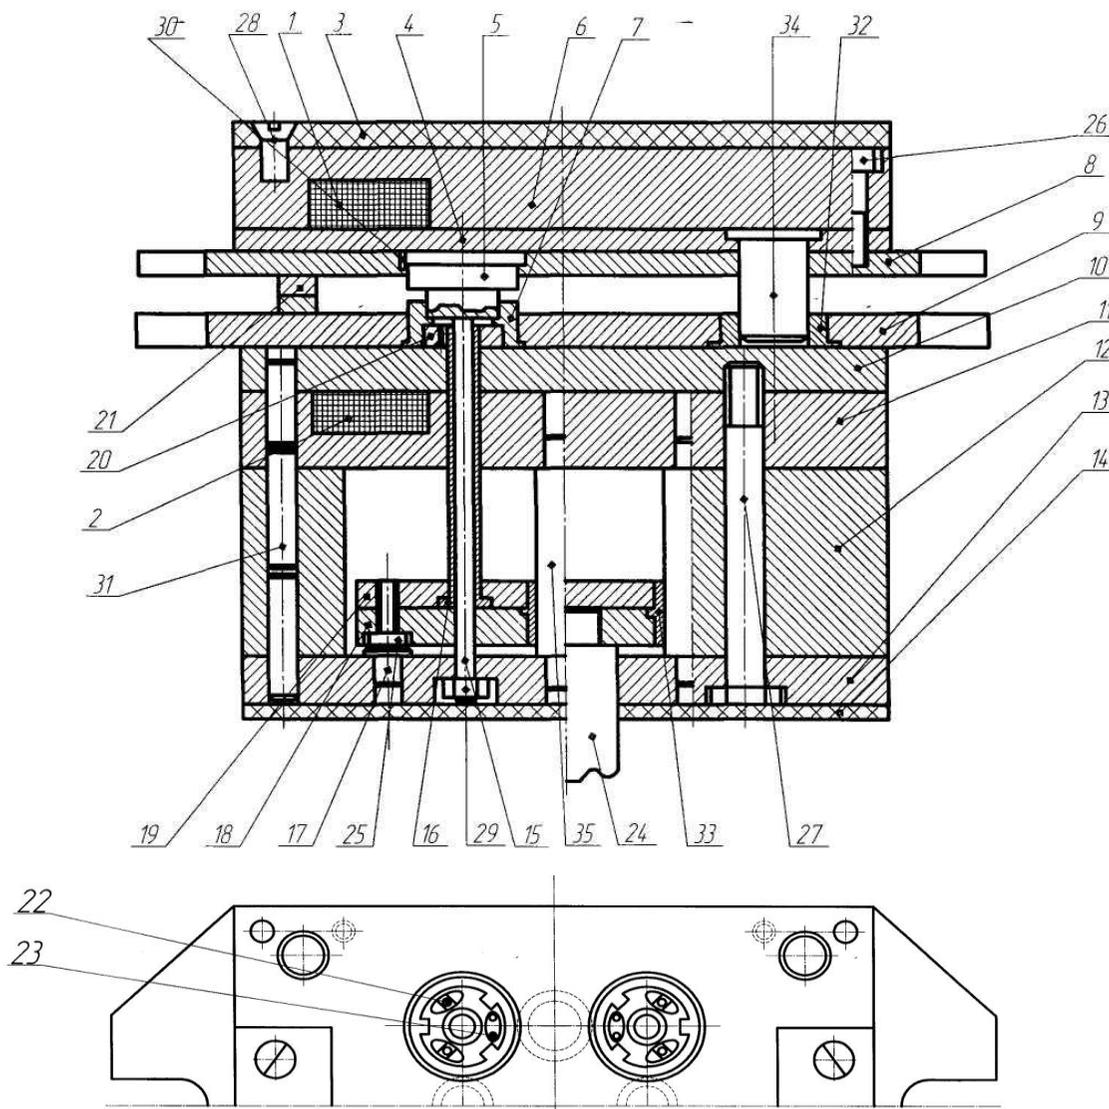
Пресс-форма для изготовления деталей методом прессования
